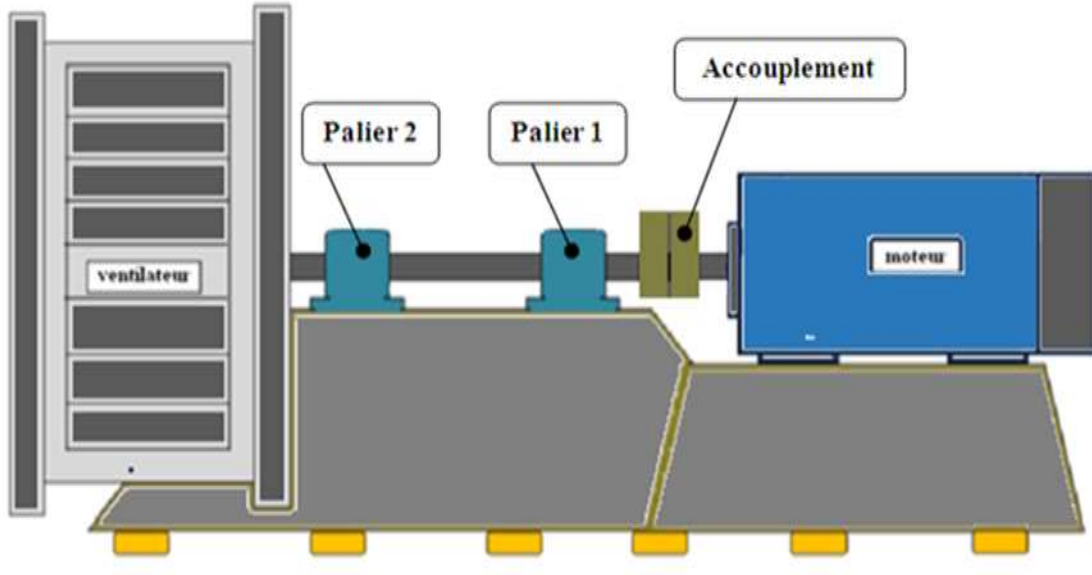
Dessin d'ensemble du rotor [6]
